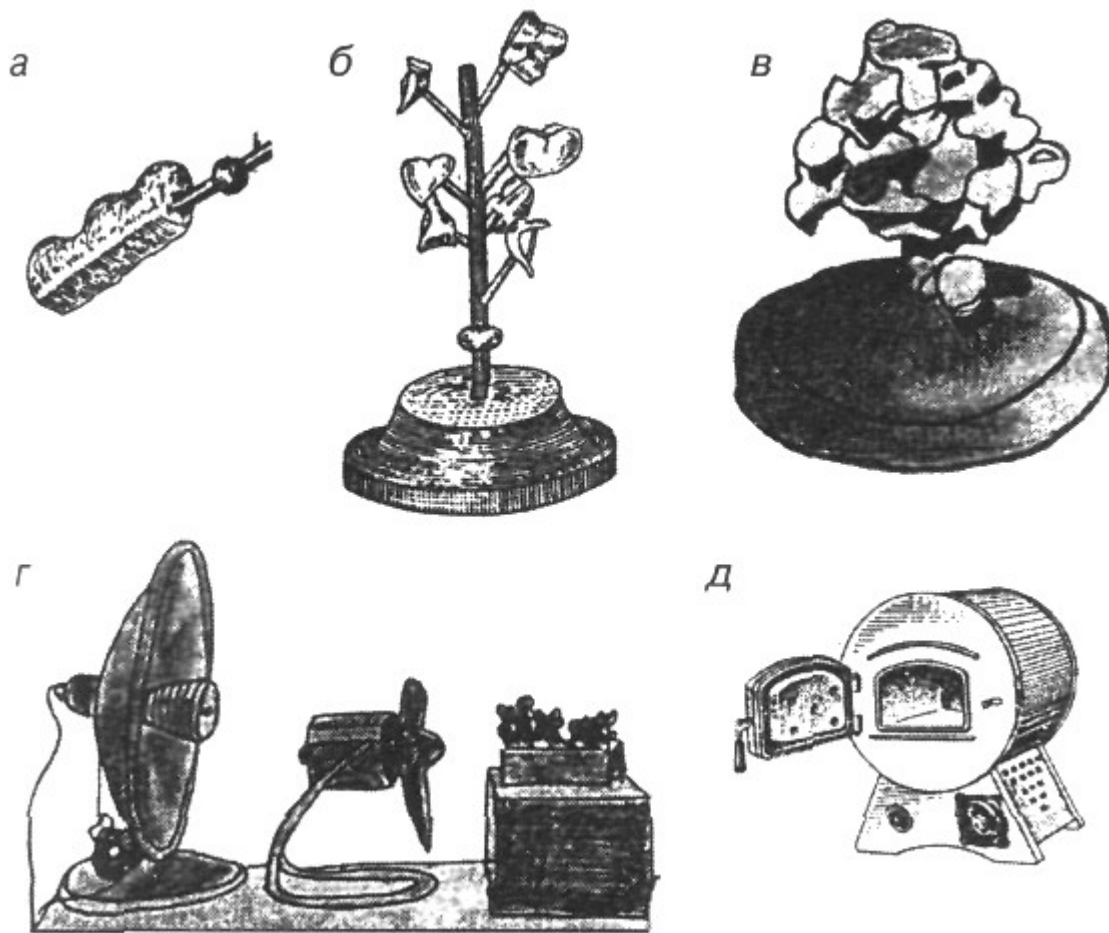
Этапы подготовки восковой модели к отливке: а – укрепление литника к восковой заготовке; б – литникообразующая система; в – нанесение облицовочной массы; г – высушивание облицовочной массы; д – муфельная печь для выплавления воска и прокаливания опоки.
